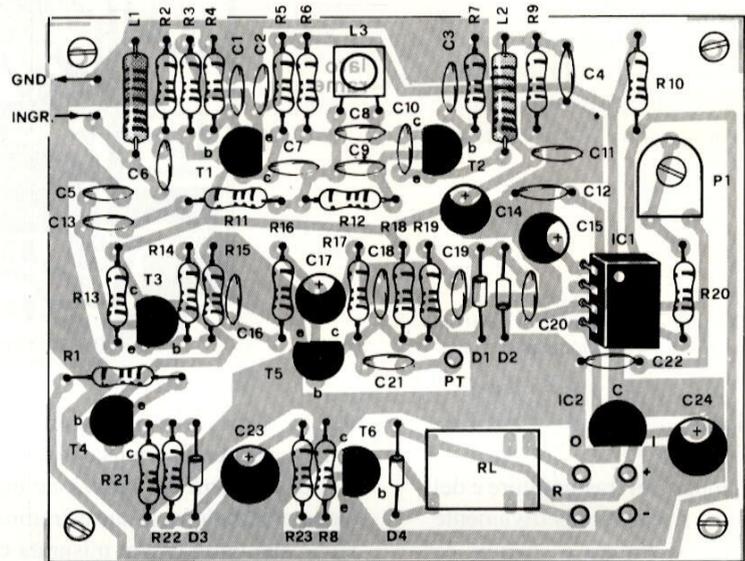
Disposizione dei componenti sul circuito stampato del ricevitore.
